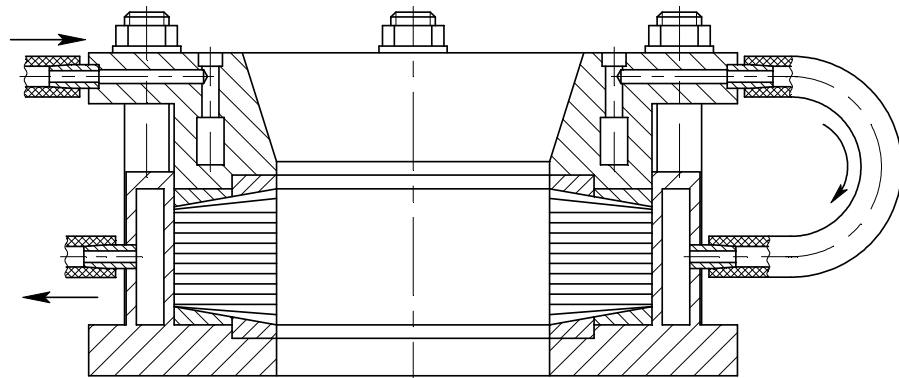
Водоохлаждаемое приспособление для сборки иглофрез
